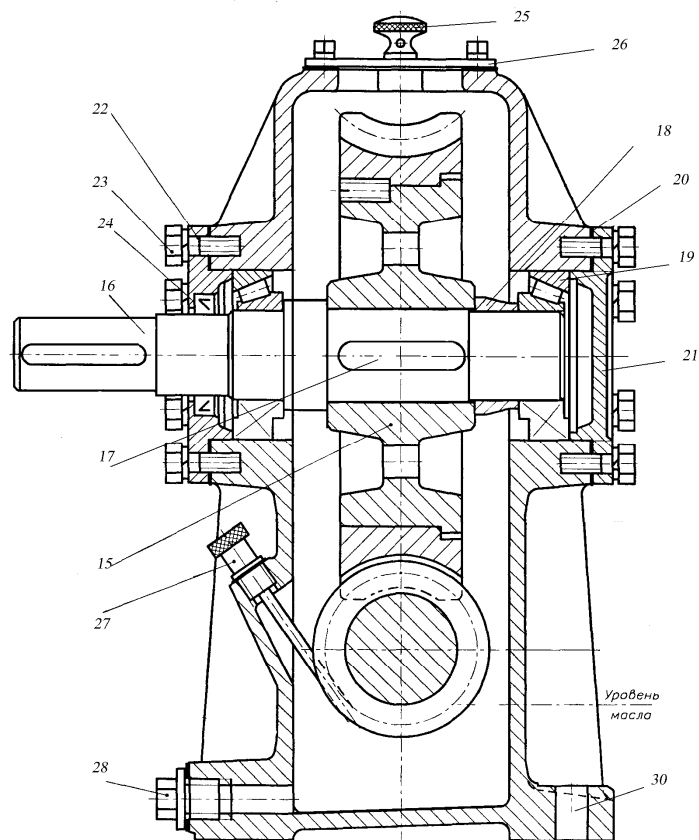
Редуктор червячный одноступенчатый (продолжение)
